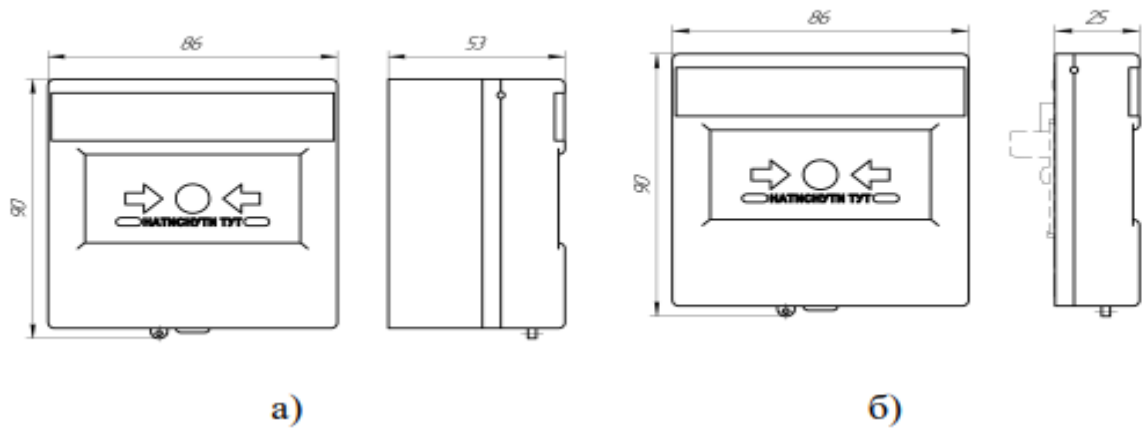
Загальний вигляд та габарити кнопок, розміри в мм
